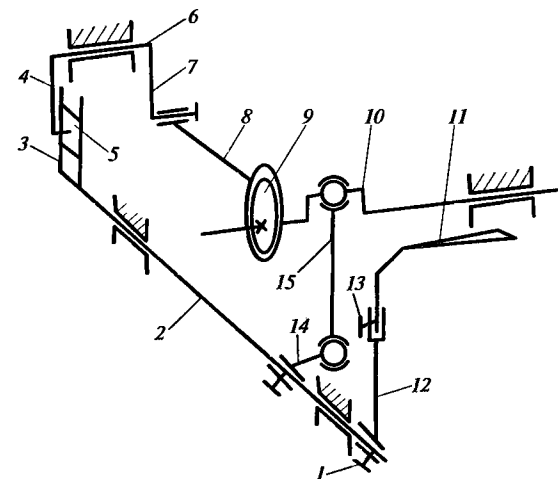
Кинематическая схема механизма петлителя для образования двухниточного цепного стежка типа 401 на краеобметочных машинах завода «Агат»
